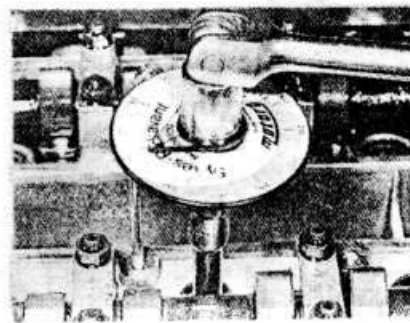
а затем поверните их на определенный угол — двигатель с двумя распредвалами
